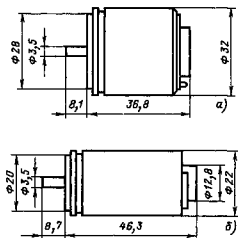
7 Габаритные и установочные размеры датчиков угла 90Д-32-3(а) и 90Д-20-1(б)
